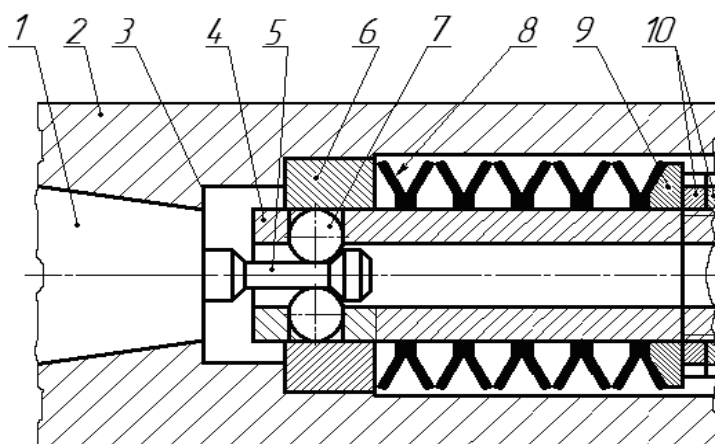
Схема зажима инструмента в шпинделе станка с помощью шариков
